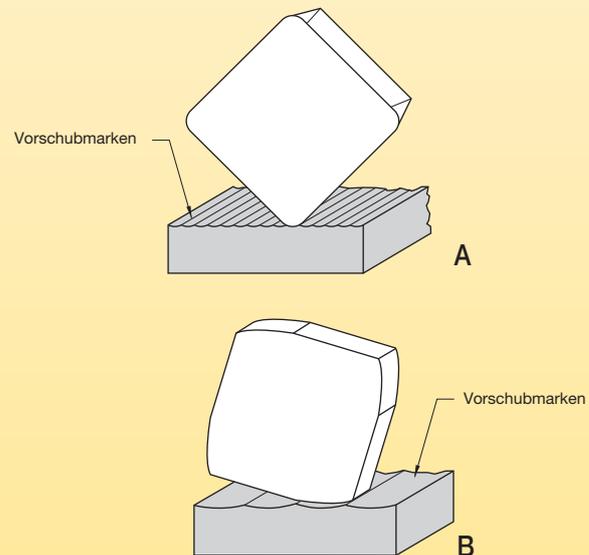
Vorschubmarken, die mit einer Vollradius-Wendeschneidplatte (A) erzeugt wurden, im Vergleich zu Marken, die mit einer Breitschlicht-Wendeschneidplatte (B) erzeugt wurden.
